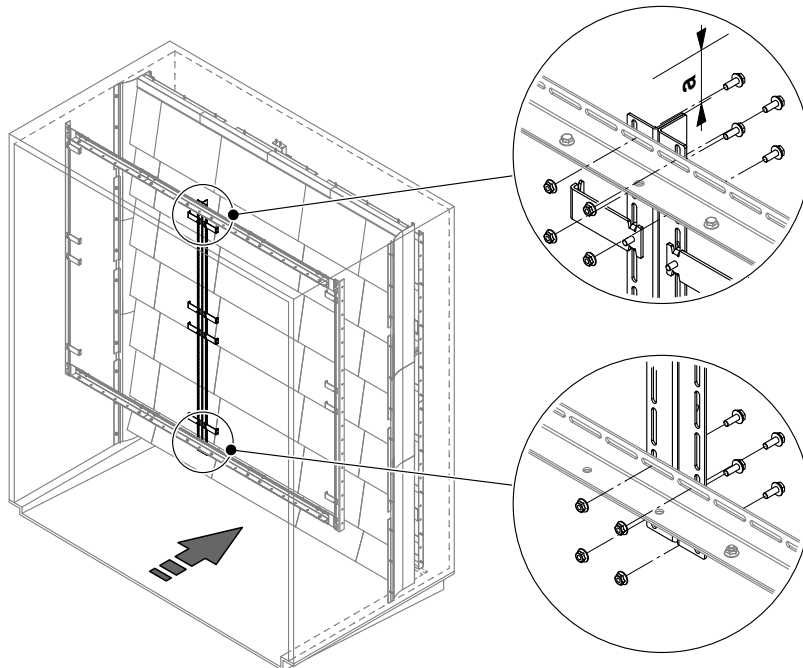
Montaje de lo(s) apoyo(s) vertical(es)
